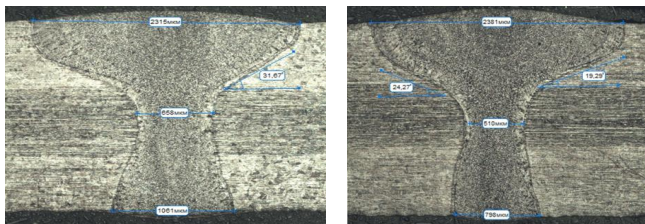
Сварные соединения, полученные при помощи лазерной сварки. [1]
